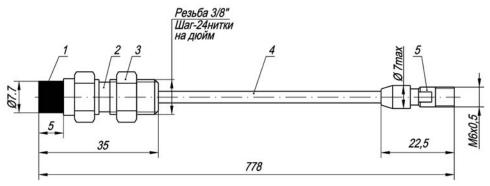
Преобразователь вихретоковый ИЦФР.408113.013 (код ПВ19): 1 – наконечник; 2 – корпус; 3 – гайка; 4 – кабель; 5 – розетка СР-50-106ФВ
